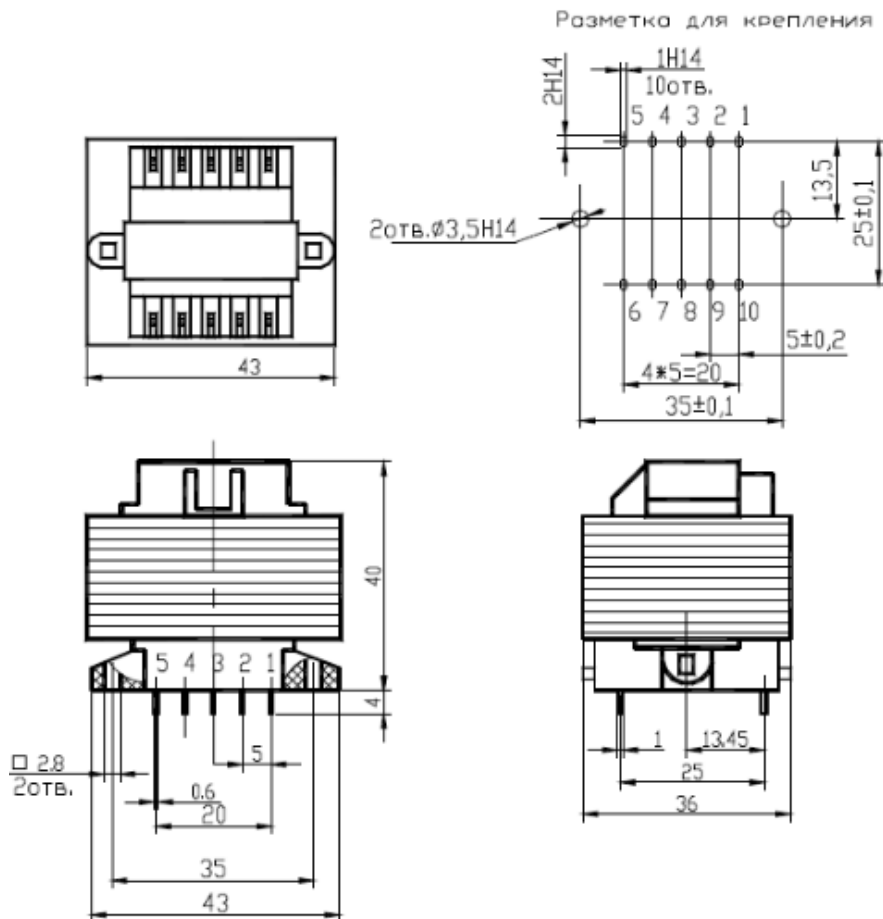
Внешний вид и размеры трансформатора ТП-112
